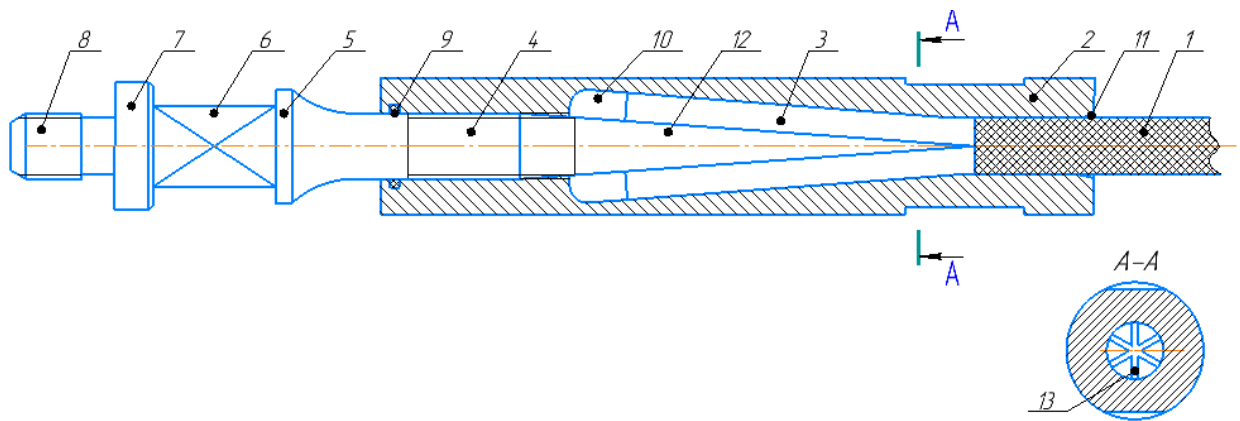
Розроблене з’єднання гібридної насосної штанги. 1 – тіло штанги, 2 – муфта з конічною внутрішньою поверхнею, 3 – кінець штанги для закріплення в муфті, 4 – різьба, 5 – бурт підделеваторний, 6 – шийка квадратна, 7 – бурт упорний, 8 – різьба; 9 – ущільнення; 10, 13 – порожнина; 11 – скруглення; 12 – конус.
